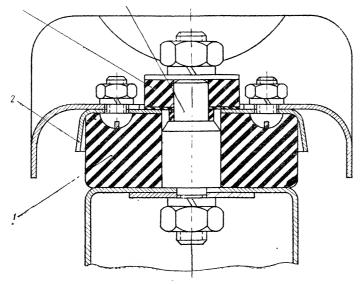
Амортизатор: 1 — резиновая подушка; 2 — крышка; 3 — резиновая шайба; 4 — штырь
